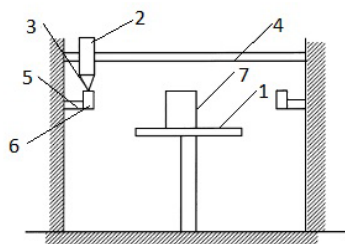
Самоочистка сопла экструдера: 1 – рабочий стол, 2 – печатающая головка, 3 – сопло, 4 – направляющая по оси Y, 5 – держатель очистителя сопла, 6 – очиститель сопла, 7 – печатающая деталь
